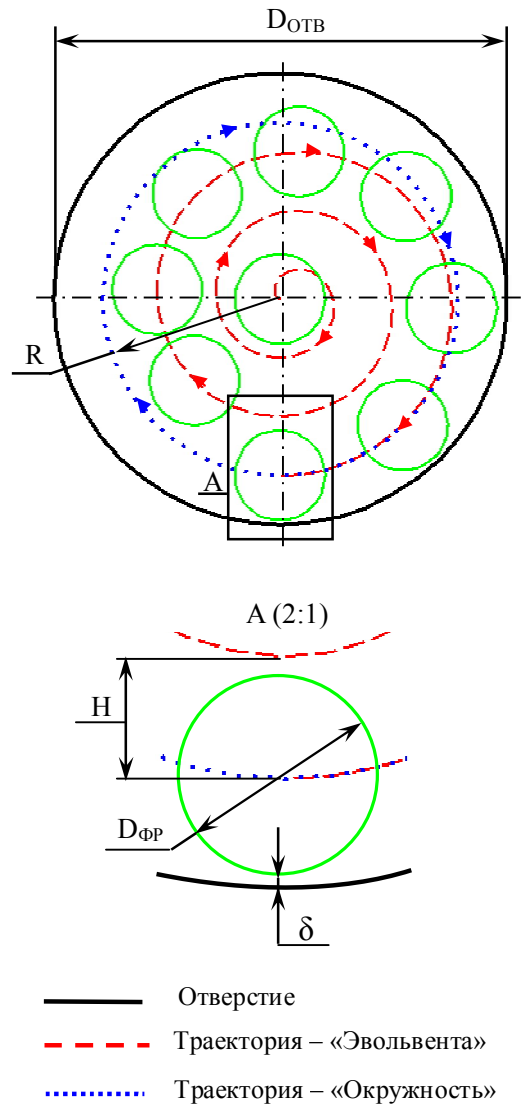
Эвольвентная траектория черновой расфрезеровки отверстия
